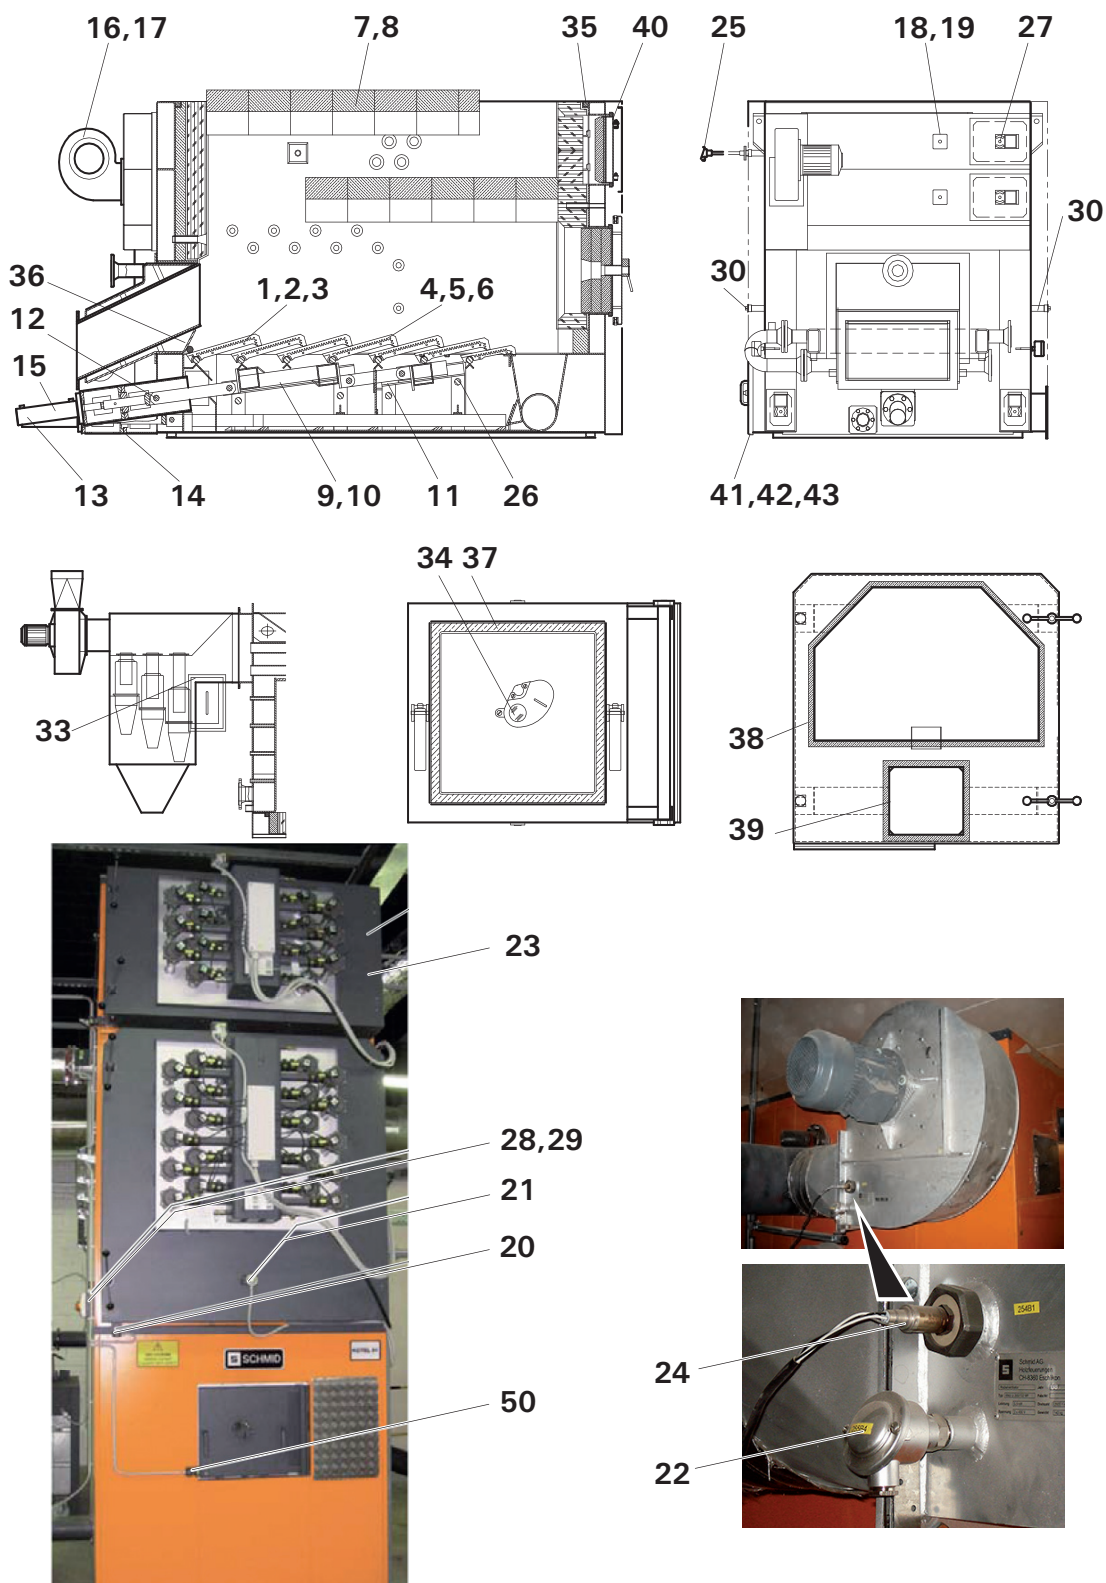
Pièces de rechange chaudière à grille mobile UTSR
